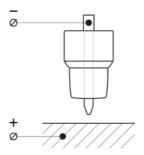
Полярность при TIG сварке.
